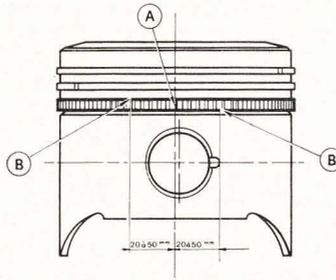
A : coupe de l'expandeur ; B : coupe des anneaux flexibles.
